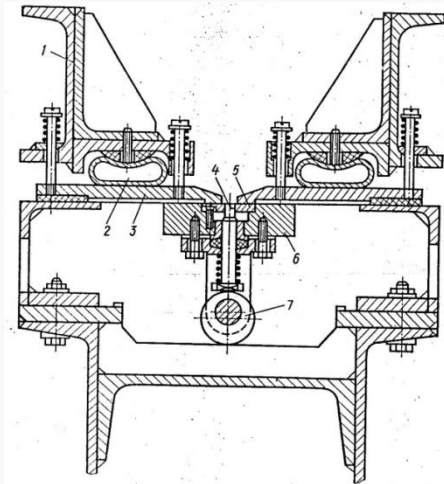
Притискний вузол складально-зварювального стану для автоматичного зварювання прямолінійних стиків тонколистових елементів
